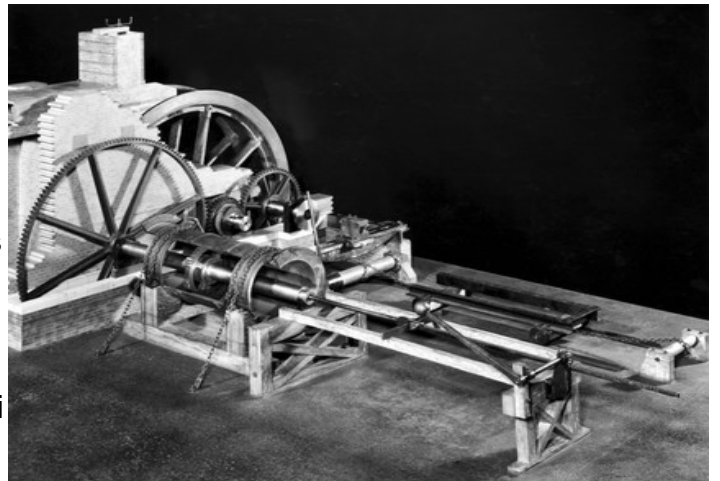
Mandrinadora construïda per Jhon Wilkinson l'any 1775
